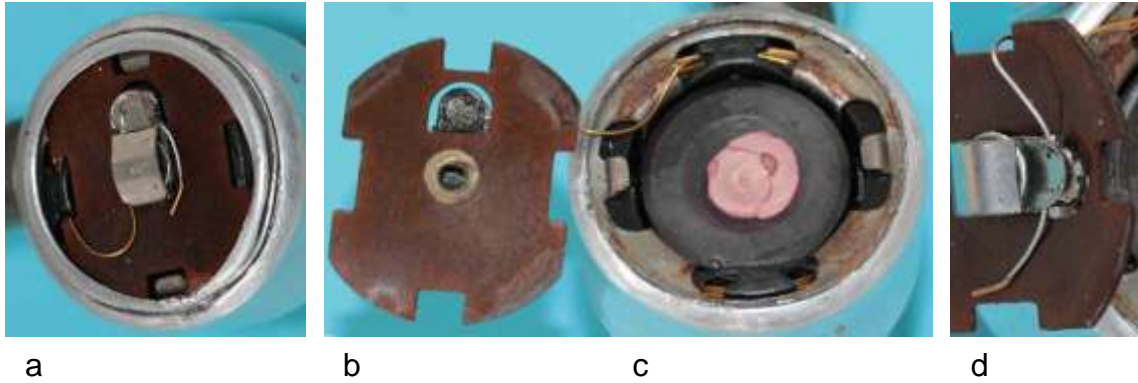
Kontaktierung: a) Mit einem Hohlblech befestigte Blattfeder, b) Oberseite der Kontaktplatte, c) Zur Blattfeder geführtes Spuleneende, d) In der Feder eingeklemmter Aluminiumdraht
